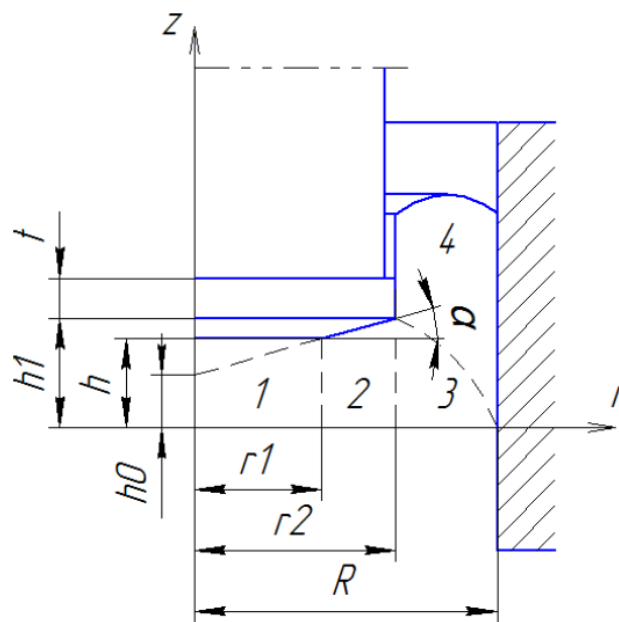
Розрахункова схема зворотного видавлювання
